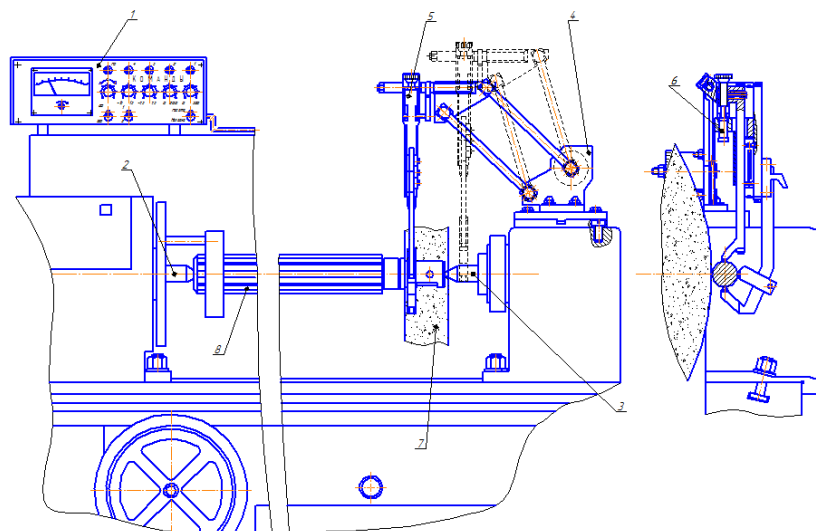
Загальний вигляд системи вимірювальної для активного контролю
